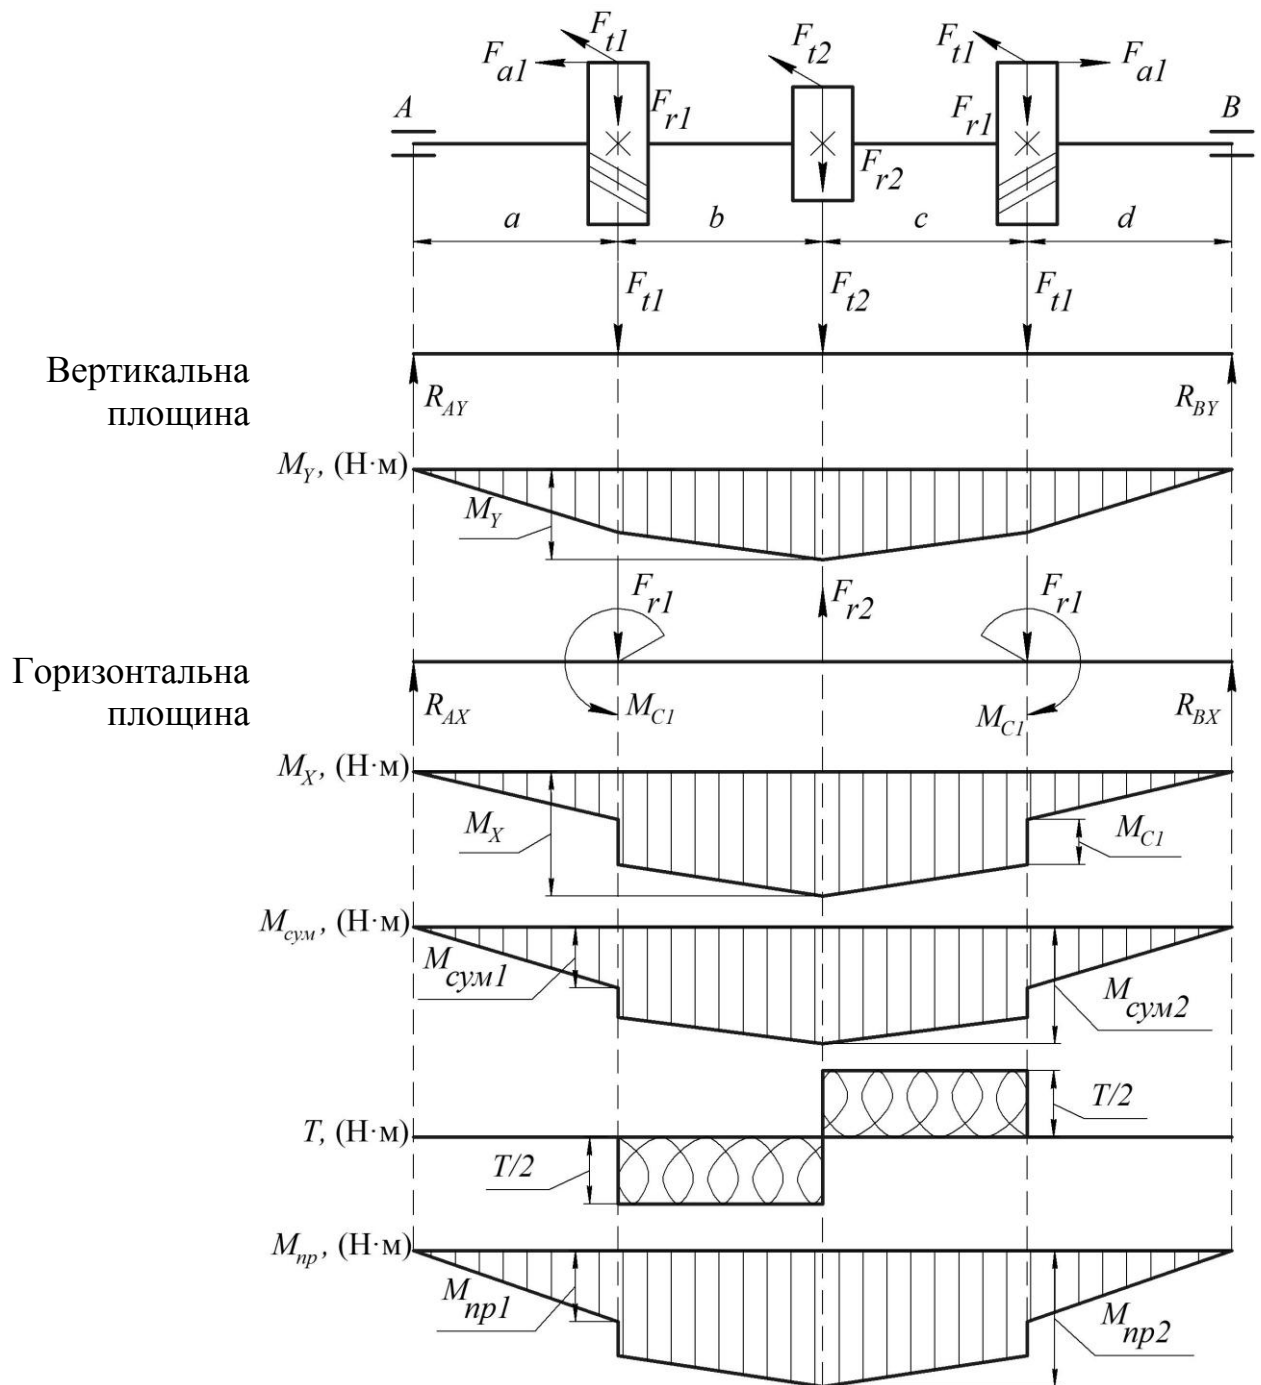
Проміжний вал двоступінчастого редуктора з шевронною зубчастою передачею
